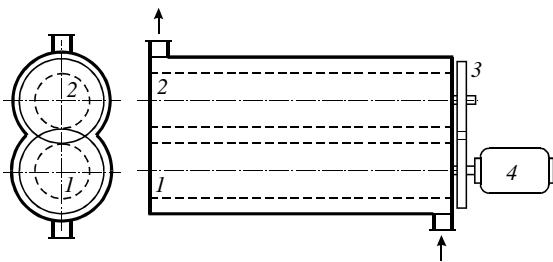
Схема винтового компрессора: 1 – ведущий винт; 2 – ведомый винт; 3 – синхронизирующие шестерни; 4 – привод
